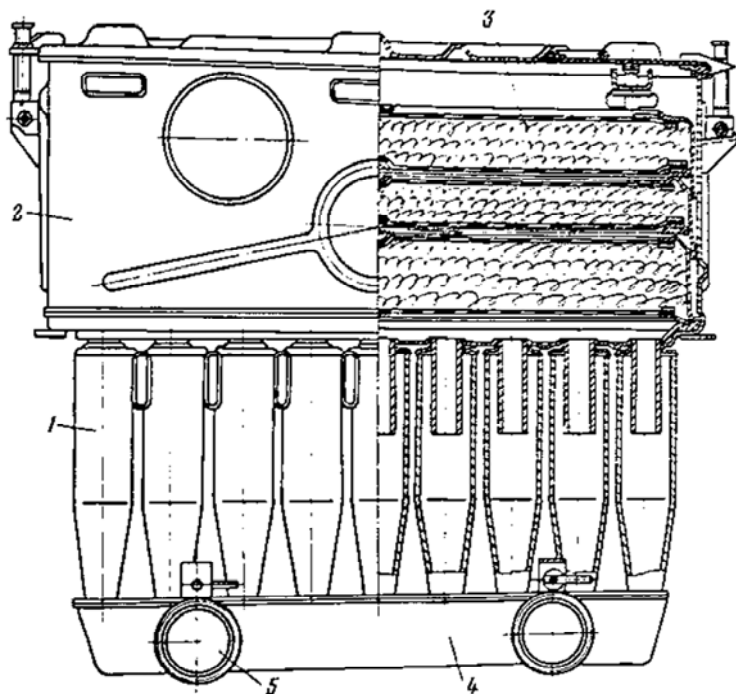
Воздухоочиститель двигателя Д12А-525А:
